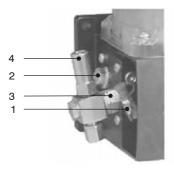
Anschluss Pumpenelemente und Druckbegrenzungsventil
